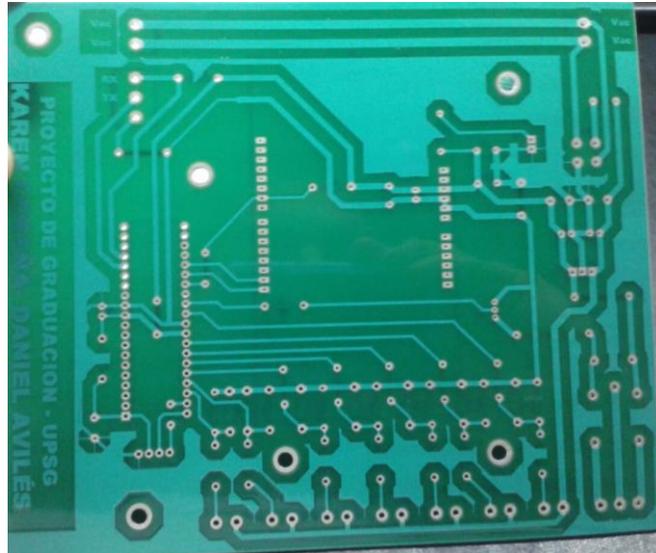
Diseño de placa maestro impresa en fibra de vidrio doble lado. Placa maestro impresa en fibra de vidrio de 17cm x 14 cm.
